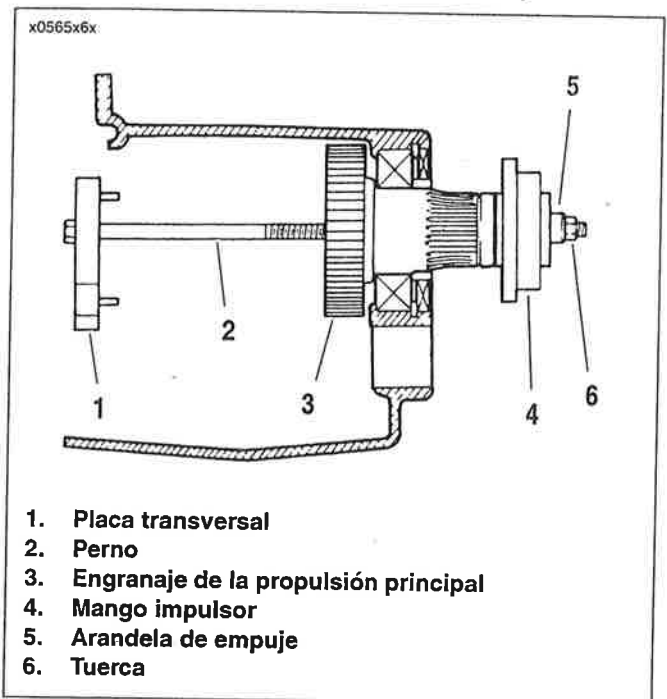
Extractor de cojinetes montaje de placa transversal (pieza N° B-45847)
